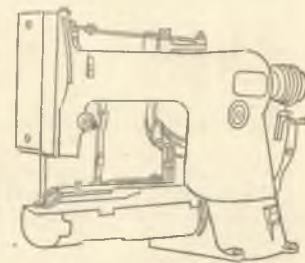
Машина-полуавтомат 1095 кл. для пришивания пуговиц
